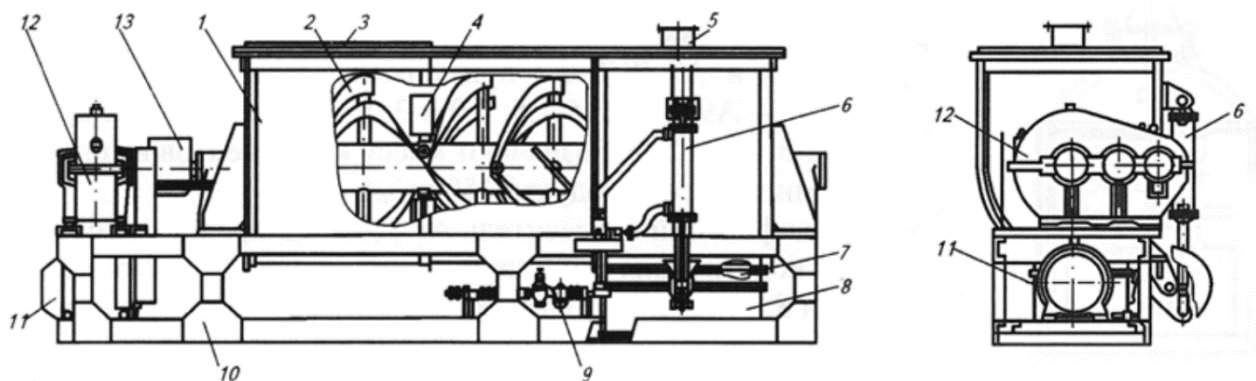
Змішувач типу СГК-1М: 1 - корпус; 2 - спіральна лопата; 3,5 - фланці; 4 - лопатка; 6 - пневмоциліндр; 7 - поворотна кришка; 8 - розвантажувальний бункер; 9 - блок повітропідготовки; 10 - станина; 11 - електродвигун; 12 - редуктор; 13 - муфта
